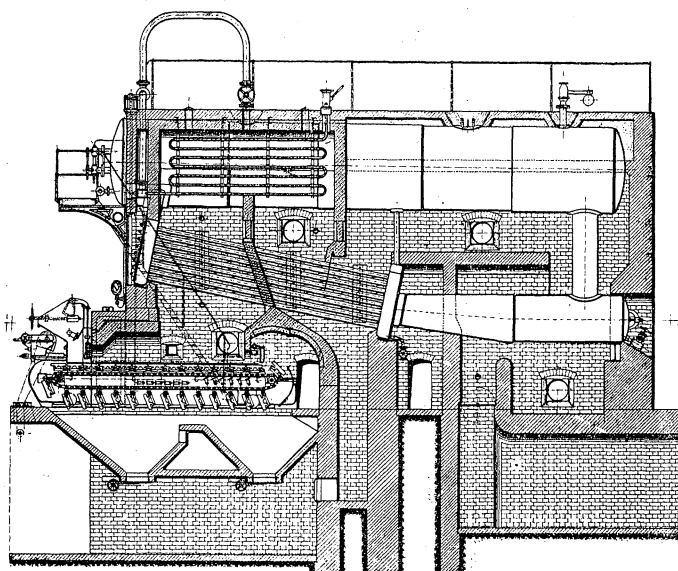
Mac-Nicol-Kessel mit Unterwind-Wanderrost.
